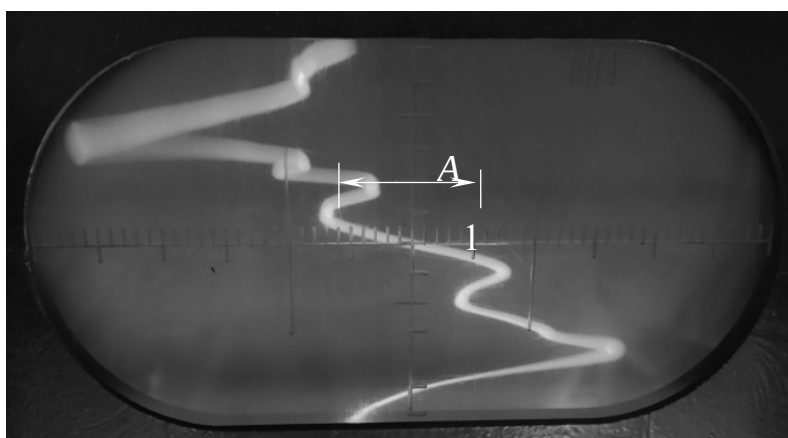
Вид сигналограммы при магнитографическом контроле сварного соединения с выпуклостью обратной стороны шва (с полным проплавлением стыка пластин)
